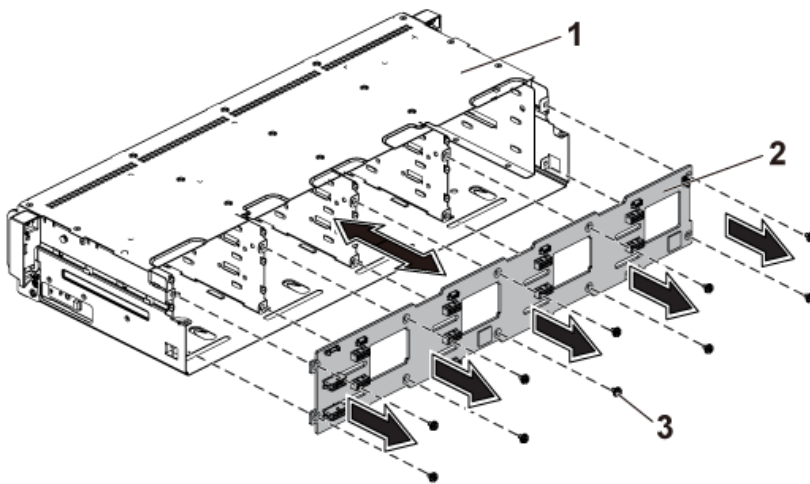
Rückwandplatine aus dem Laufwerkgehäuse entfernen und im Laufwerkgehäuse installieren
